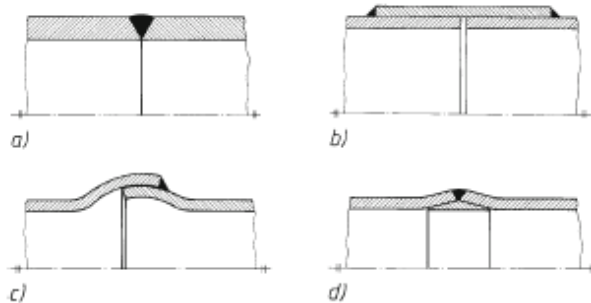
Geschweißte Rohrverbindungen.
